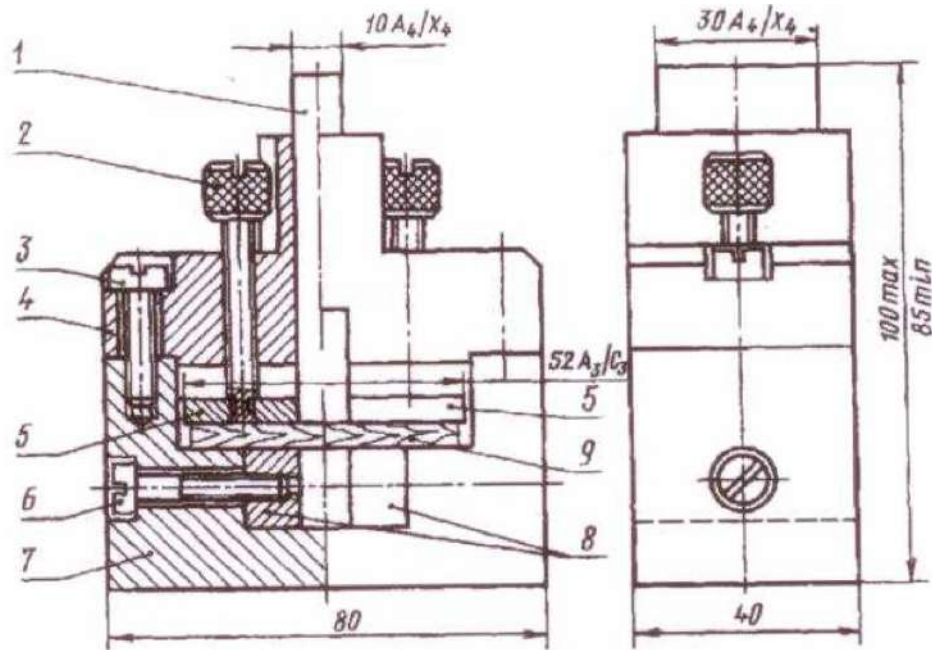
Приспособление для испытания образца древесины при перерезании поперек волокон: 1 – подвижной нож; 2 – винт зажима образца; 3 – винт крепления крышки; 4 – крышка; 5 – зажимная планка; 6 – винт установки неподвижного ножа; 7 – корпус; 8 – неподвижный нож; 9 – образец
